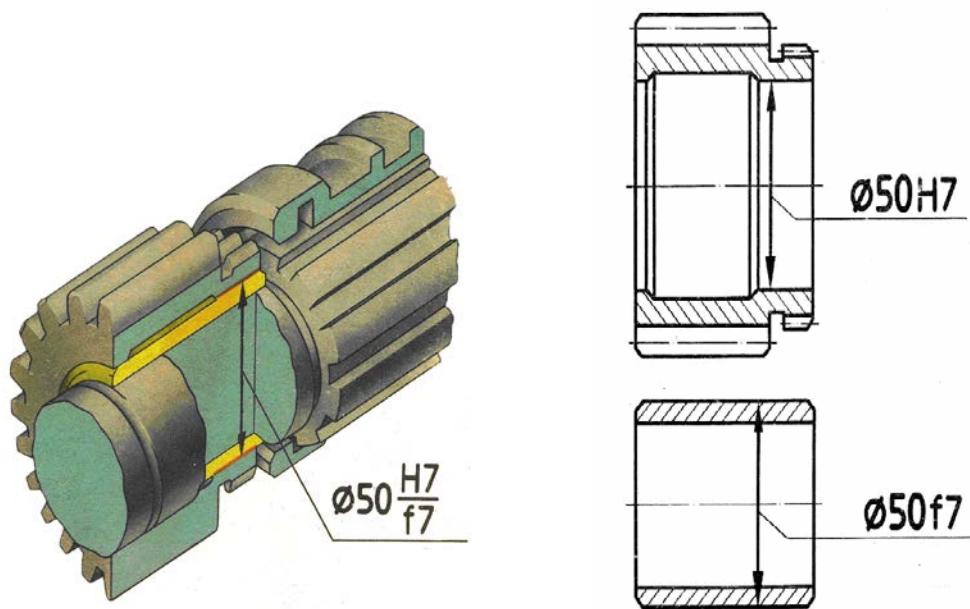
Свободно сидящее зубчатое колесо на втулке вала расточного станка
